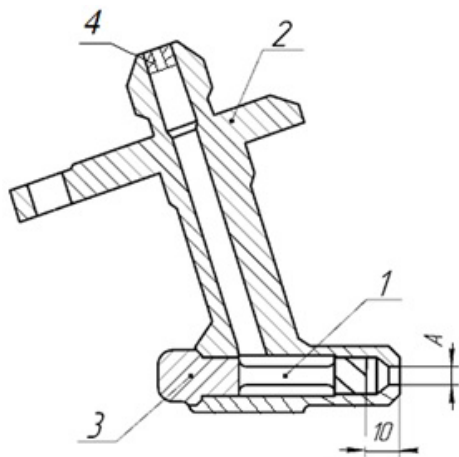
Конструкция форсунки: 1 — шнек; 2 — корпус форсунки; 3 — гайка (заглушка); 4 — дросселирующая шайба
